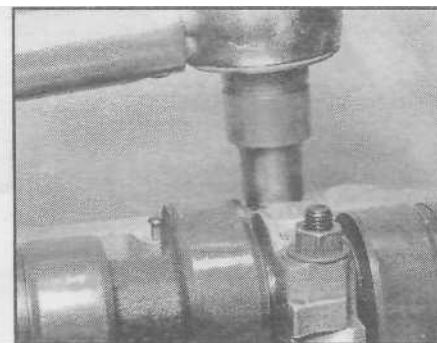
Затягивание гайки крышки подшипника распределительного вала
